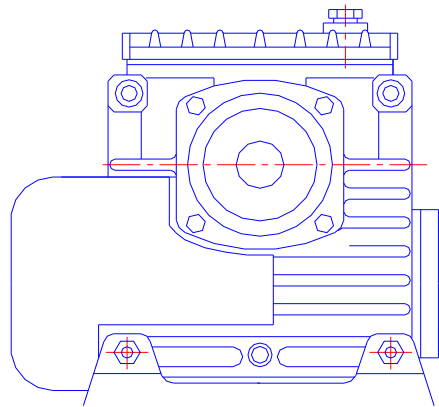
червячный редуктор 2Ч-40-50-51-3-У3 ТУУ 29.1 24587
